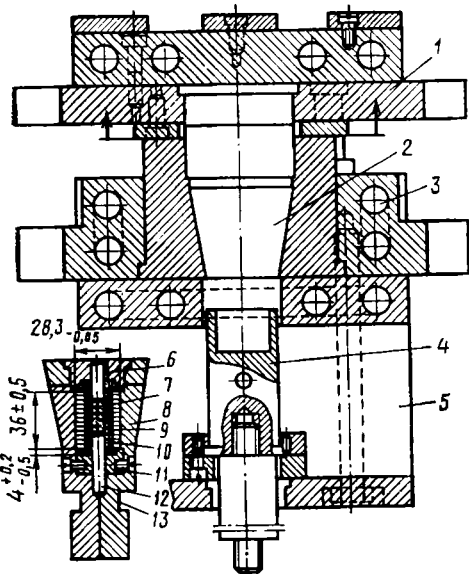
Пресс-форма для скрепления вала и сердечника пластмассой:
